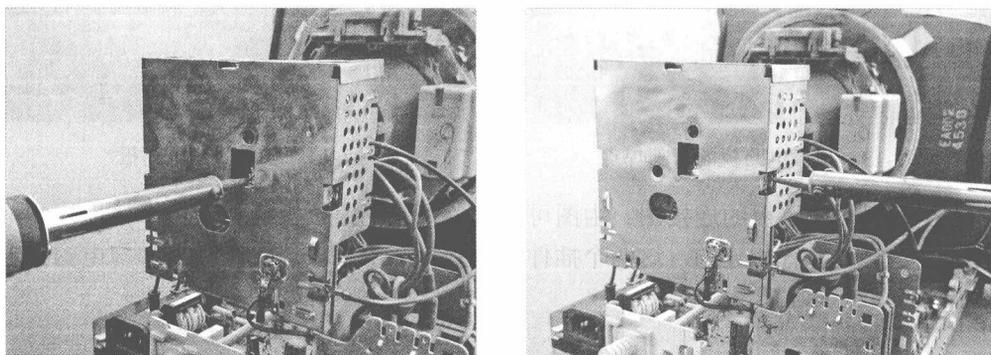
焊掉显像管座焊点上的焊锡
